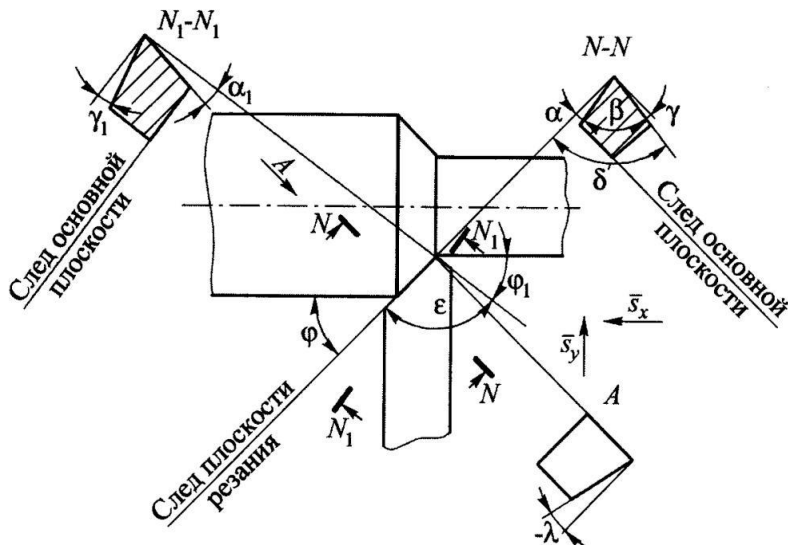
Геометрические параметры режущей части токарного проходного резца
